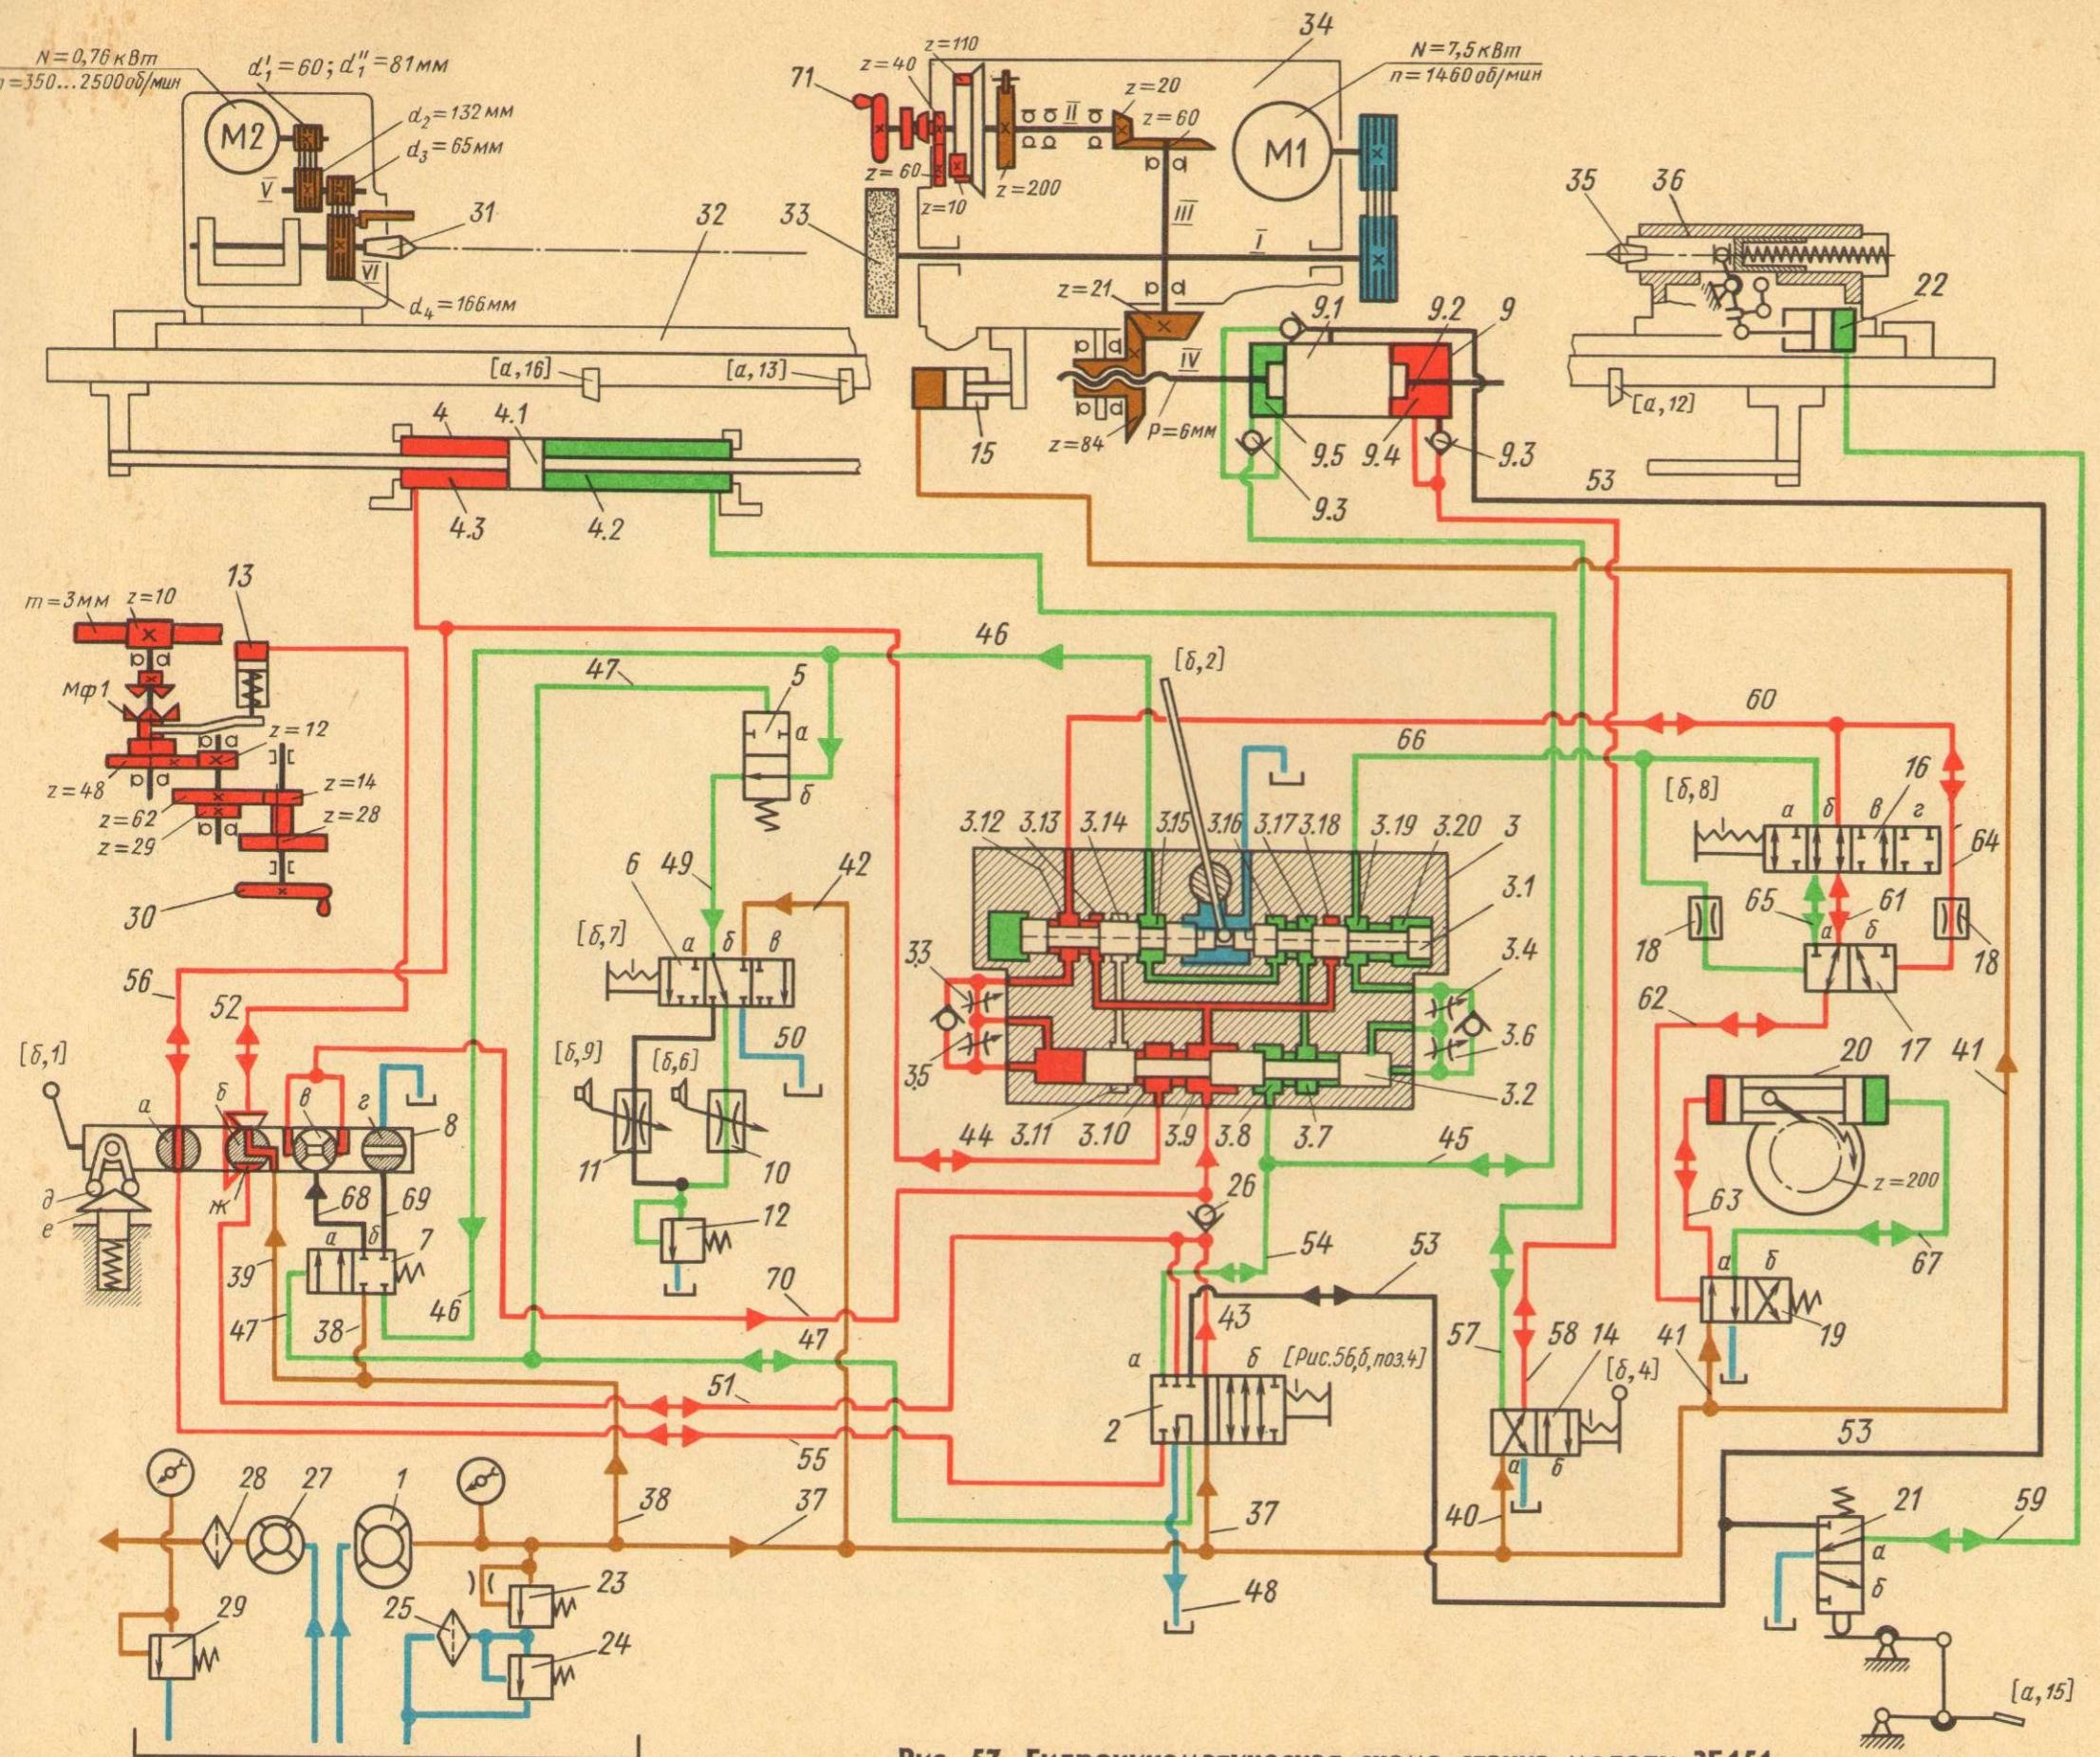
Гидрокинематическая схема станка модели ЗБ151
